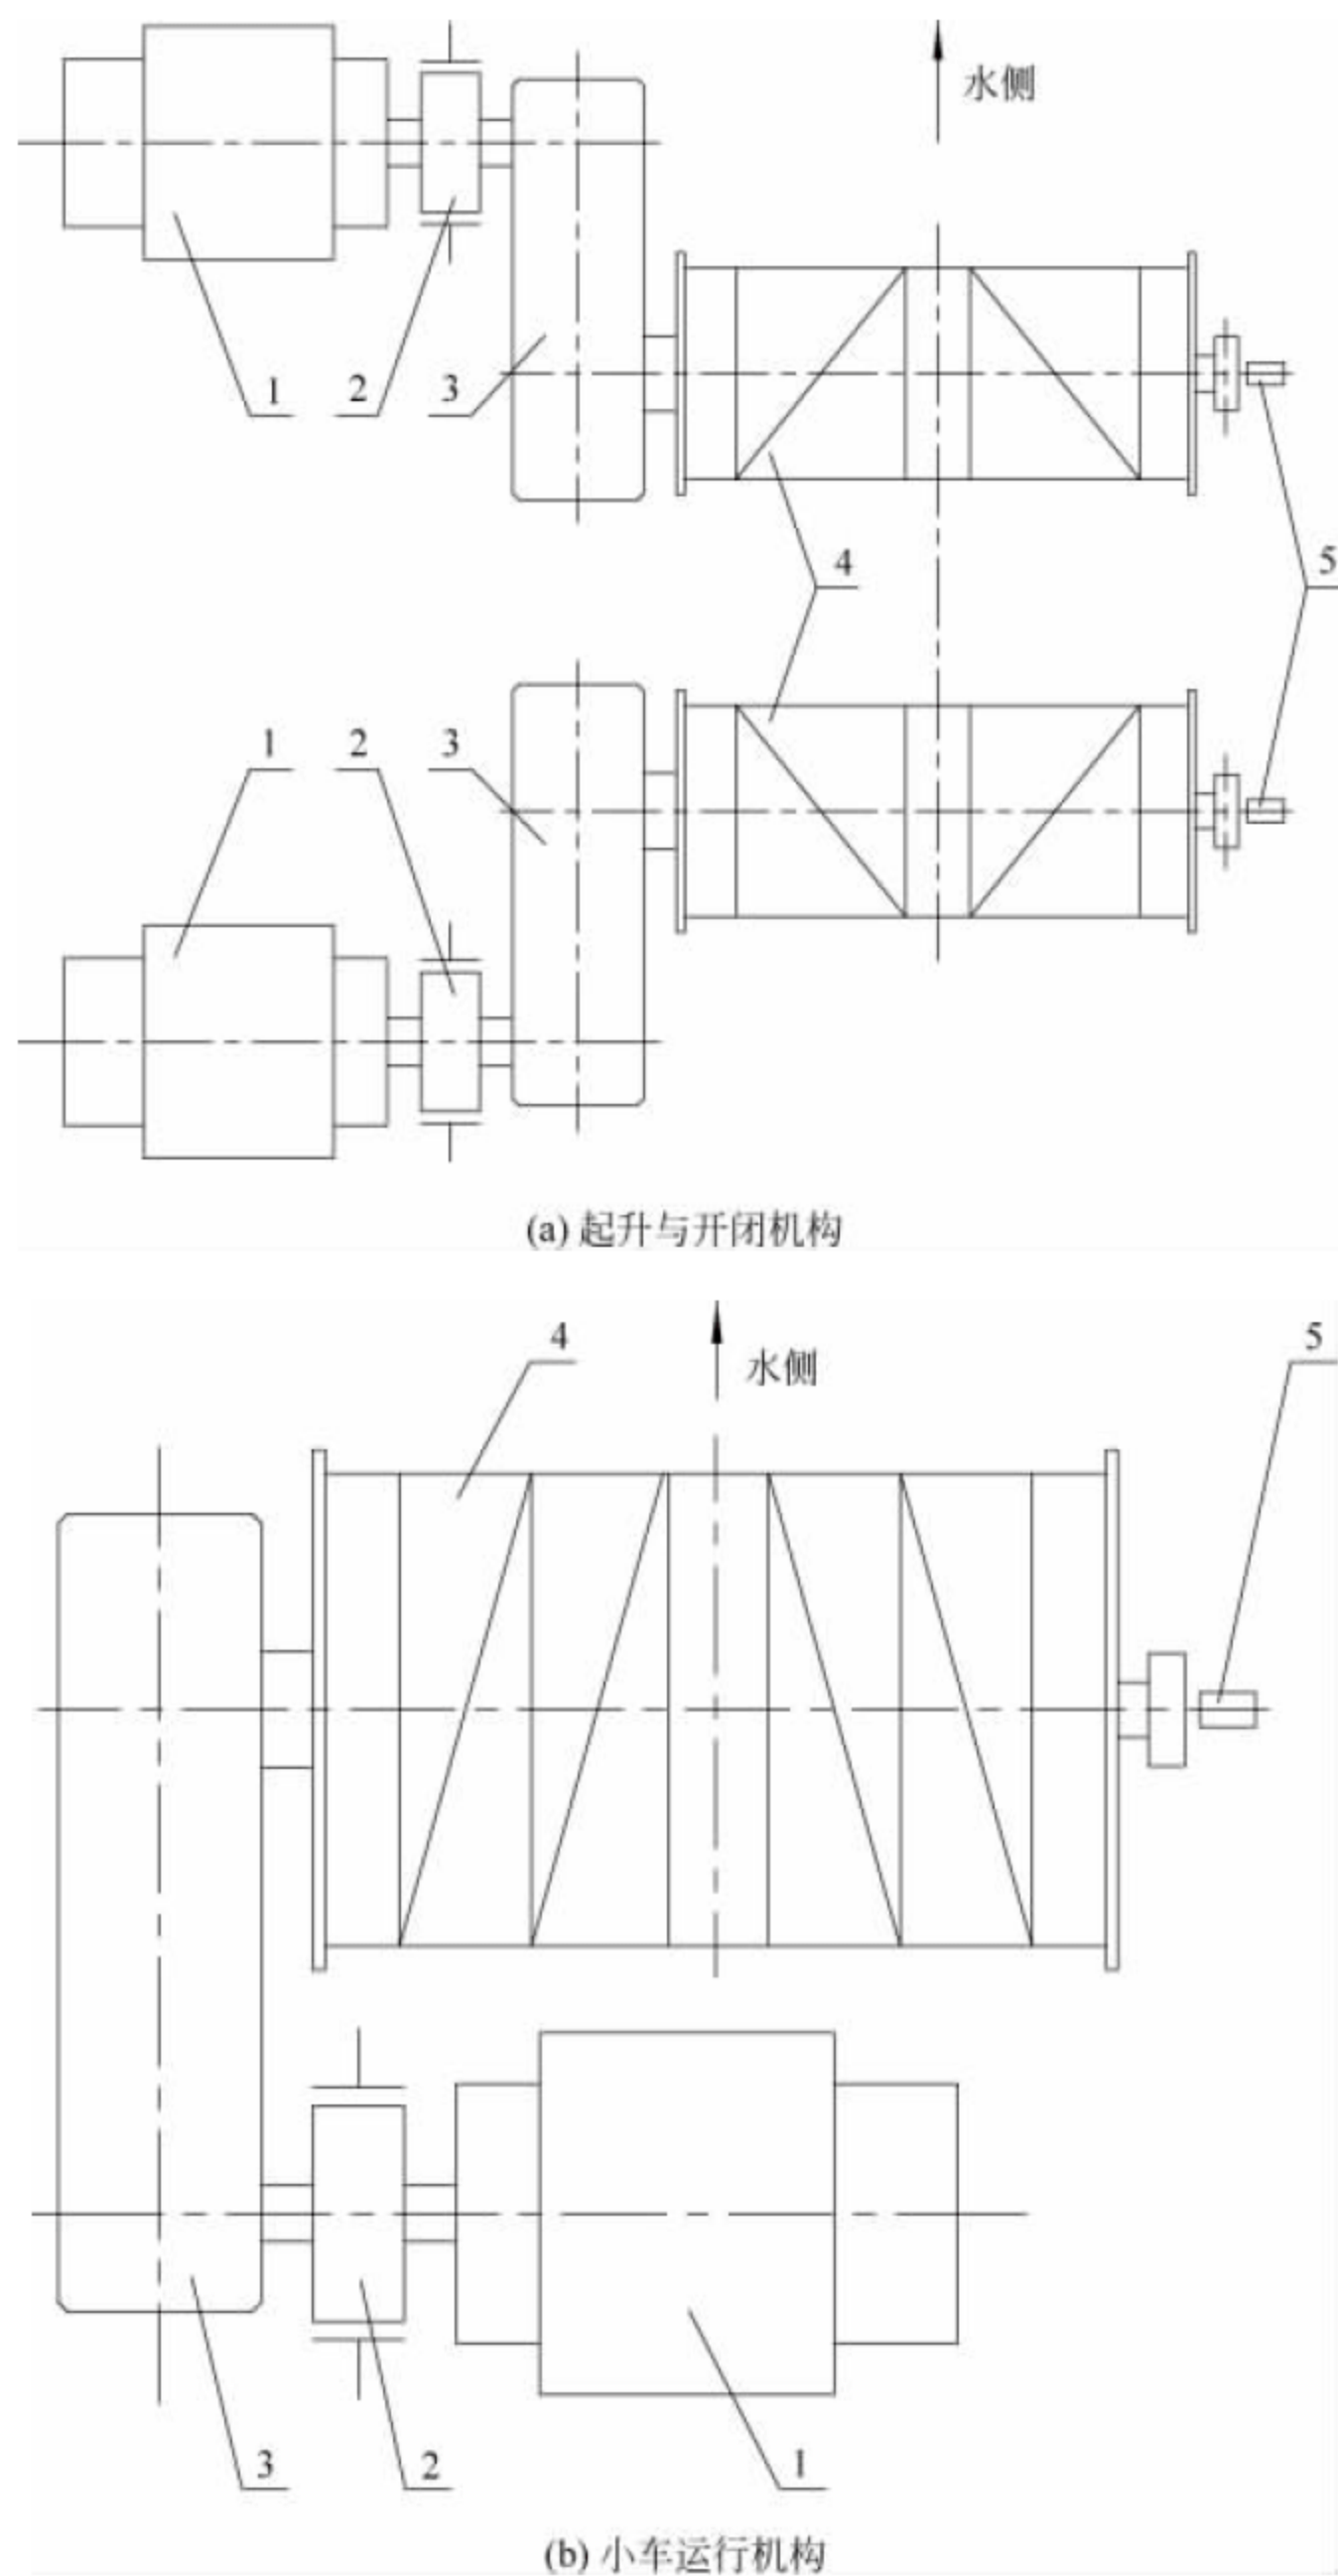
补偿小车式卸船机工作机构平面布置示意图
